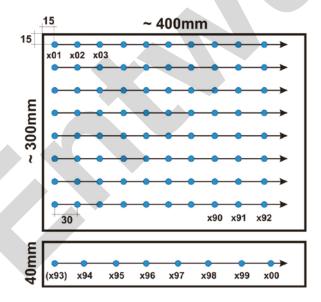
Schweißfolge bei der Ermittlung der Elektrodenstandmenge Figure 4: Weld sequence in electrode life test
